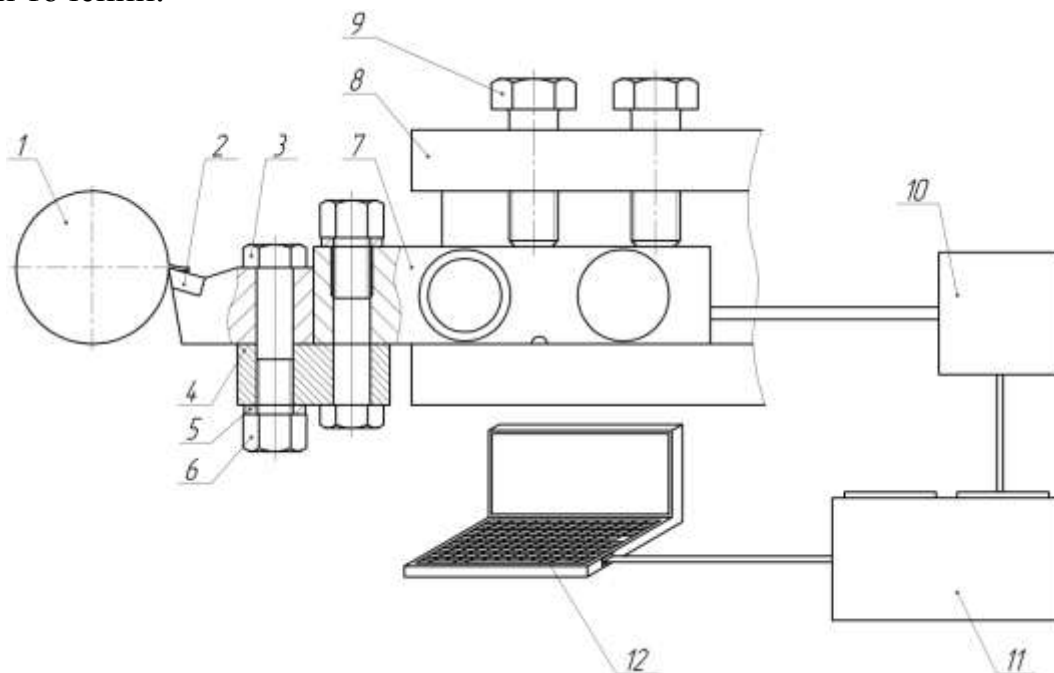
Схема установки для измерения силы резания: 1 – обрабатываемая деталь; 2 – резец; 3 – болт М12; 4 – струбцина; 5 – шайба; 6 – гайка М12; 7 – балочный тензодатчик SBA; 8 – резцедержатель; 9 – винты резцедержателя; 10 – усилитель сигнала датчика; 11 – плата сбора данных NI USB 6210; 12 – персональный компьютер
